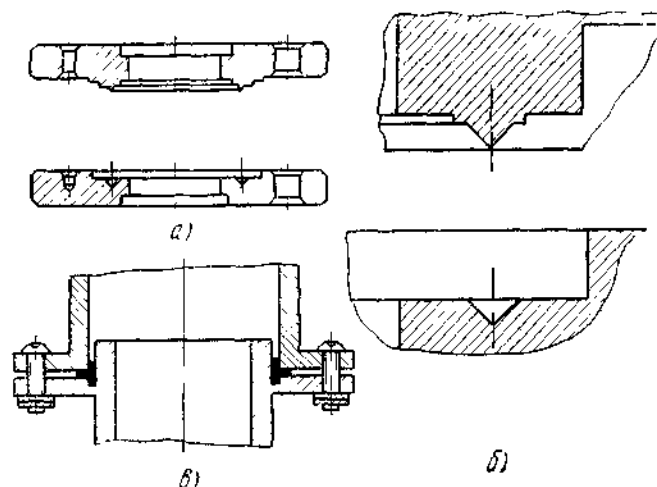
Схемы фланцевых соединений с металлическими уплотнителями
